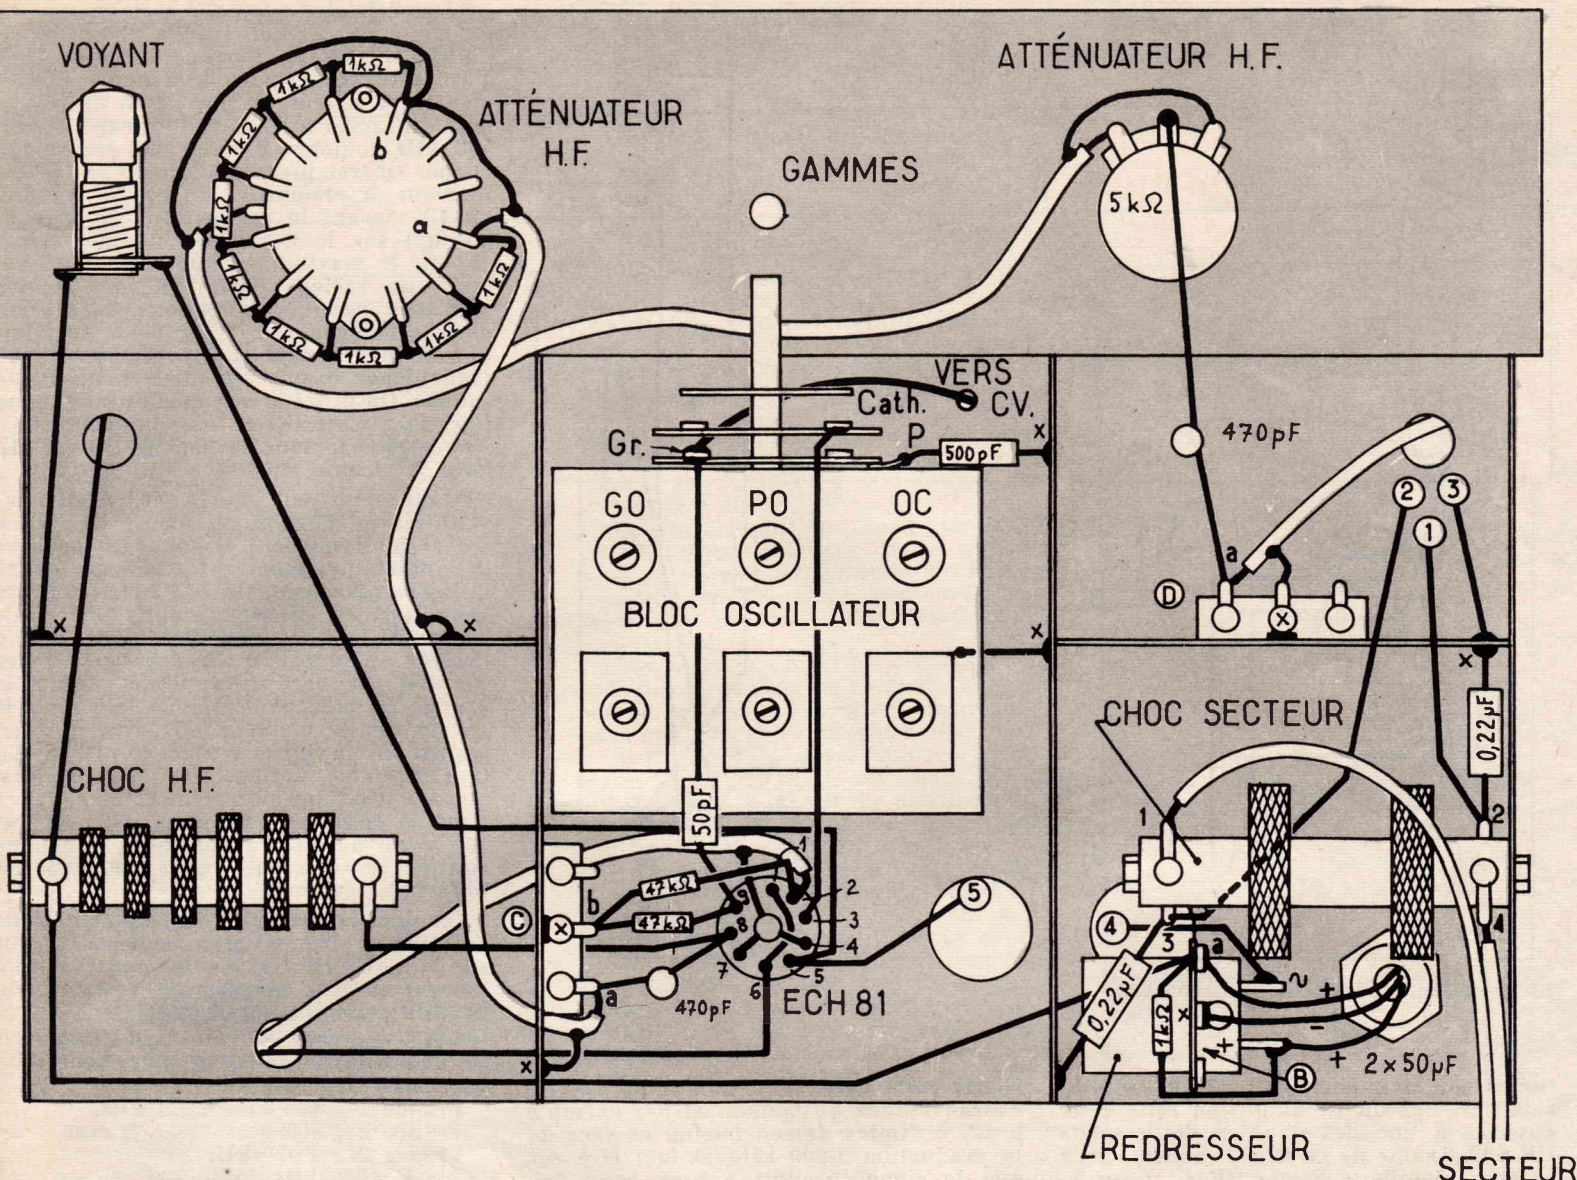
CABLAGE DU DESSOUS DU CHASSIS
